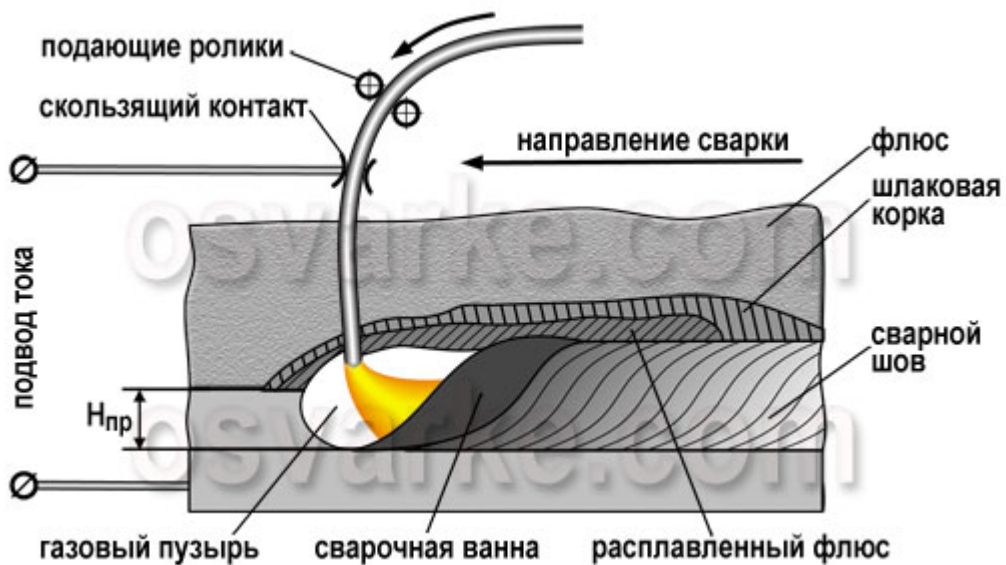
Схема процесса сварки под флюсом
